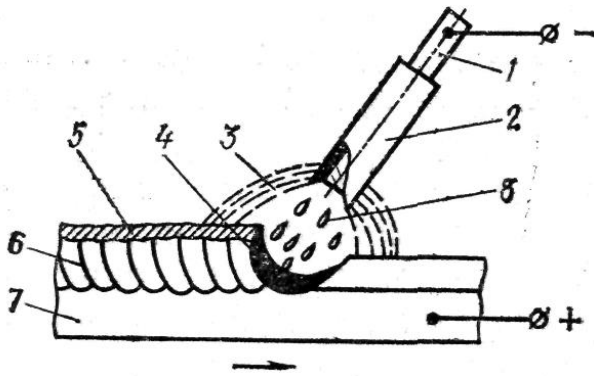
Ручная дуговая сварка металлическим электродом с покрытием (стрелкой указано направление сварки) 1 – стержень электрода; 2 – покрытие электрода; 3 – газовая защита; 4 – сварочная ванна; 5 – шлаковая корка; 6 – сварной шов
